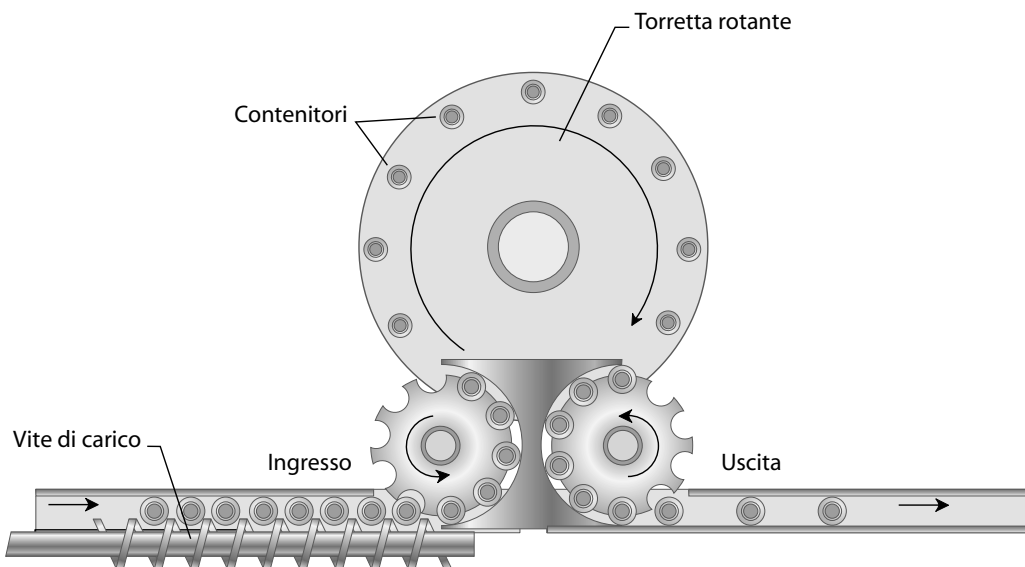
Schema di impianto di riempimento rotativo (vista dall'alto).
